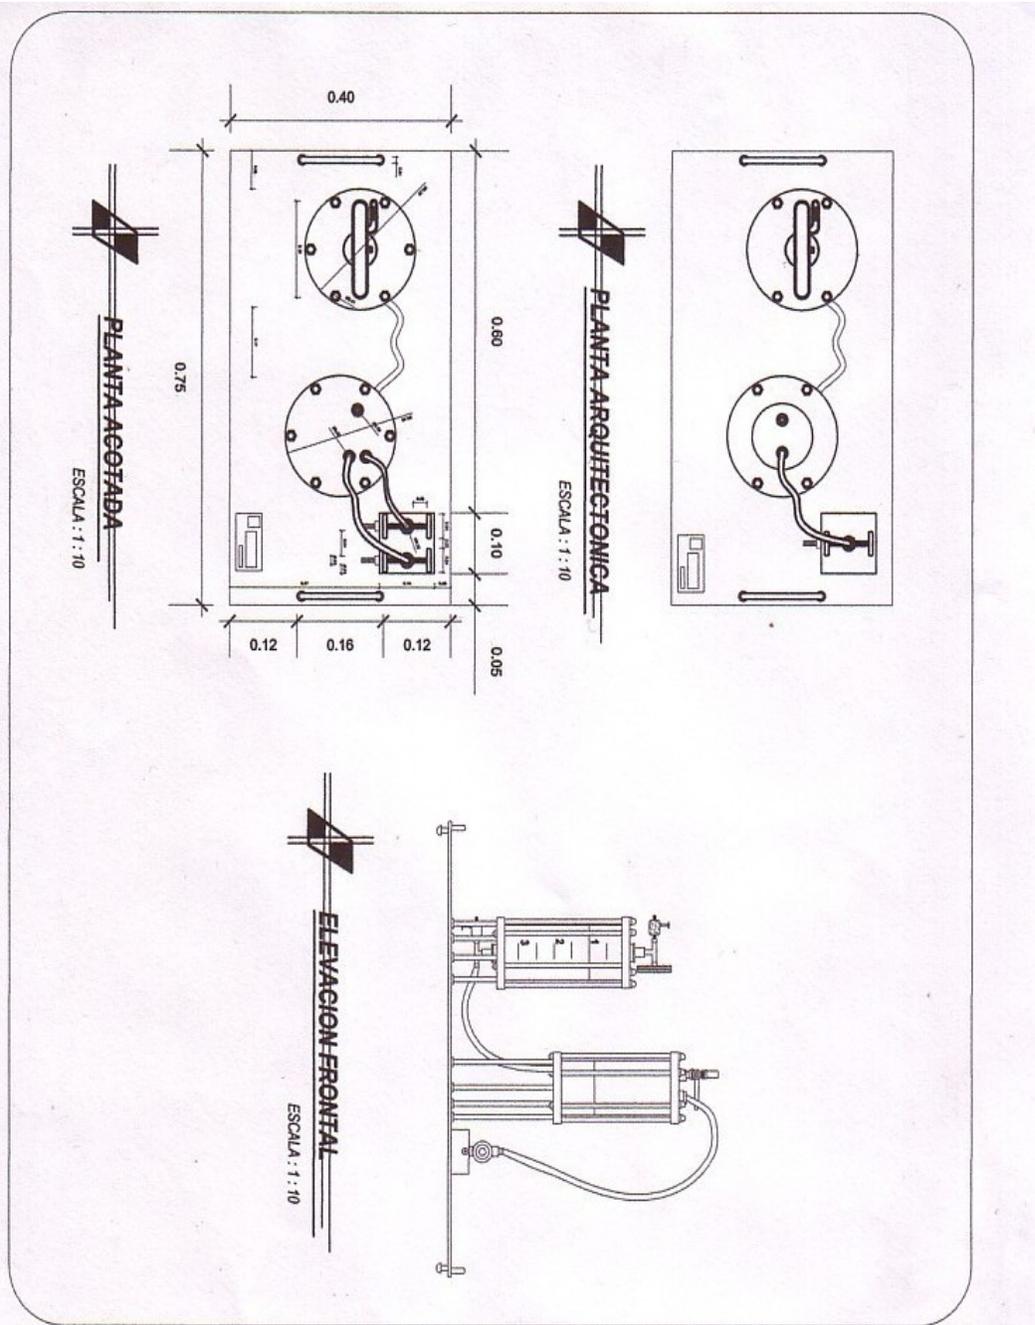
Plano final del equipo "Boyle-Méndez Primero".
